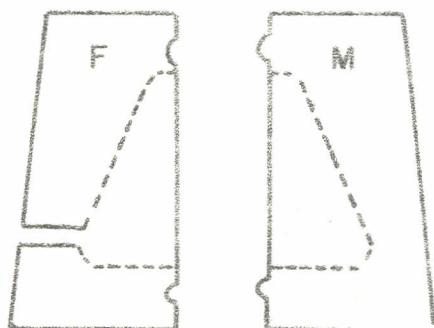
Corte longitudinal no molde de gesso utilizado na fabricação das cápsulas porosas.
